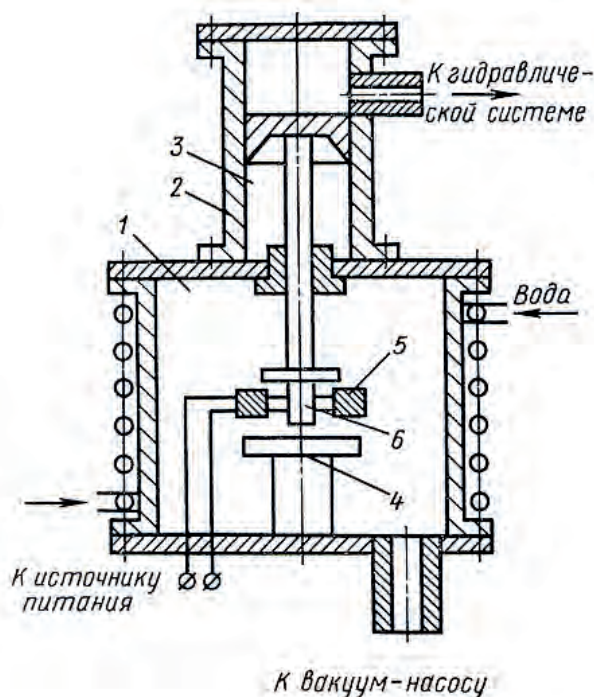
Принципиальная схема установки для диффузионной сварки в вакууме: 1 – вакуумная камера, 2 – цилиндр гидропривода, 3 – поршень, 4 – стол для крепления деталей, 5 – индуктор, 6 – свариваемые детали
